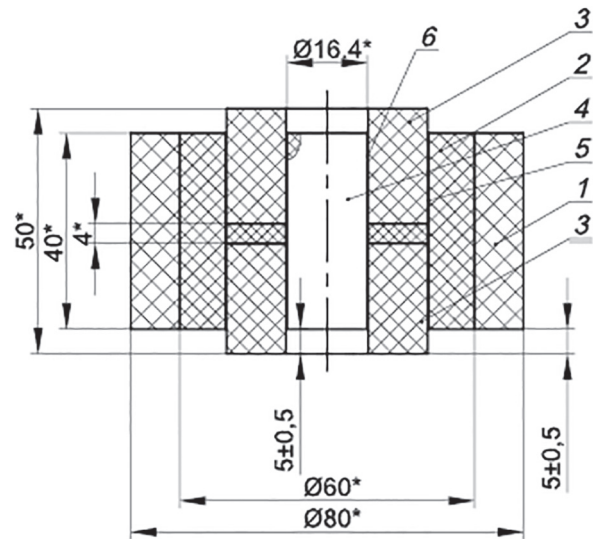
Эскиз пресс-формы в сборе для получения кольца 41,8x16,8x4:
